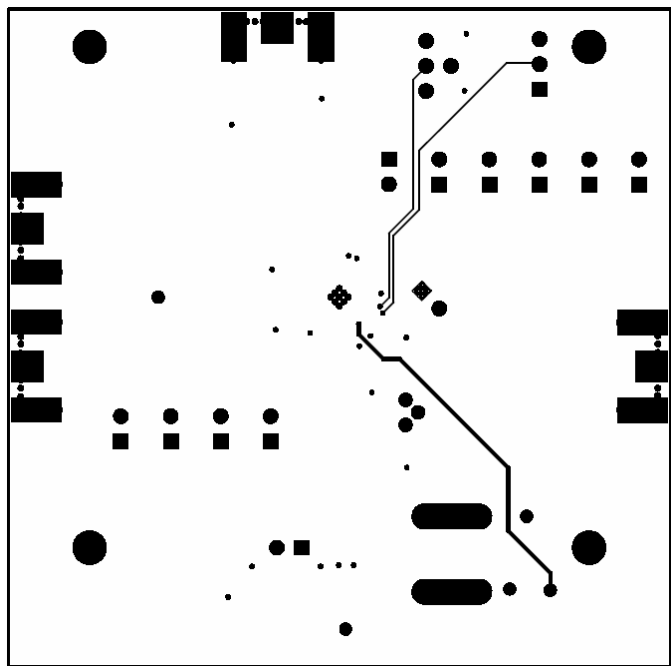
MAX3905 の EV キットの PCB レイアウト—半田面
